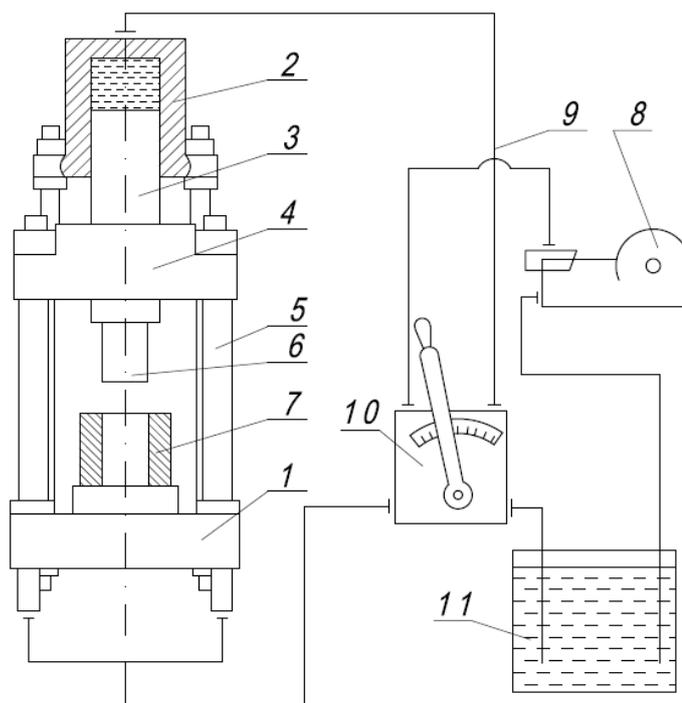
Гидропрессовая установка: 1- станина пресса; 2-гидроцилиндр; 3-главный плунжер; 4-верхняя поперечина; 5-цилиндр обратного хода; 6-пуансон; 7-контейнер; 8-насос высокого давления; 9-трубопровод высокого давления; 10-распределительное устройство (дистрибутор); 11-сливной бак.
